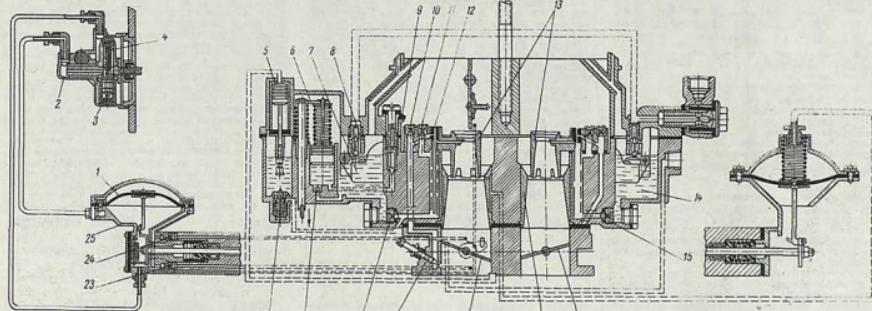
Схема четырехкамерного карбюратора К-114Б с пневмоцентробежным ограничителем оборотов и пневмальным приводом вторичных заслонок: 1 — диафрагма; 2 — впускной клапан; 3 — регулировочный винт; 4 — пневматический привод экономайзера; 5 — поплавок; 6 — воздушный клапан; 7 — распылитель ускорительного насоса; 8 — воздушный жиклер холостого хода; 11 — воздушный жиклер главной системы; 12 — топливный жиклер хол-
